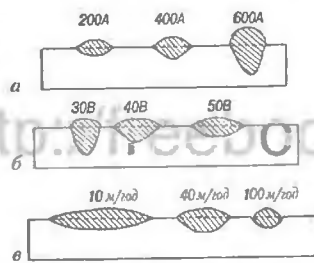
Вплив сили зварювального струму (а), напруги дуги (б), і швидкості зварювання (в) на геометричні розміри і форму шва
